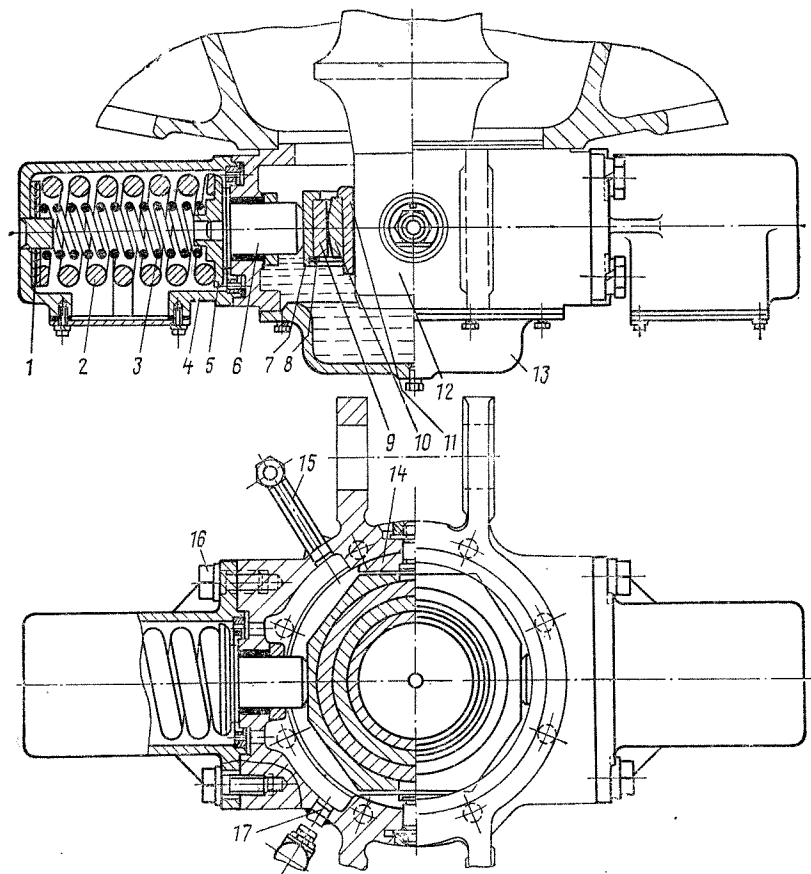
Шкворневой узел электровоза ВЛ10 с боковыми опорами кузова
